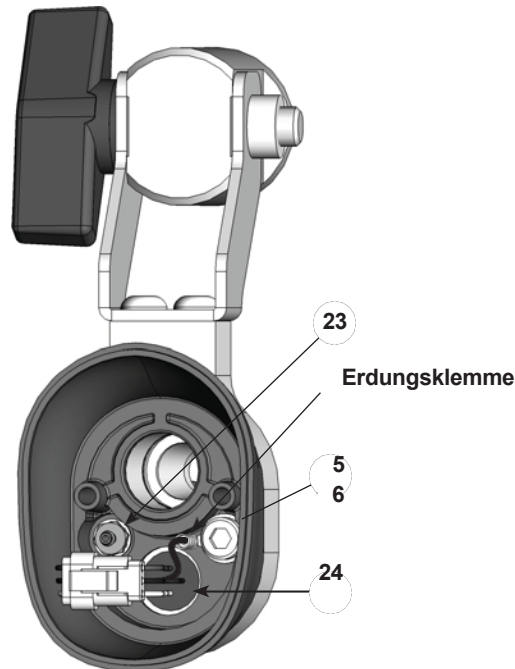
Demontage der Pistole – Austausch von Kabelbuchse und Stecknippel
